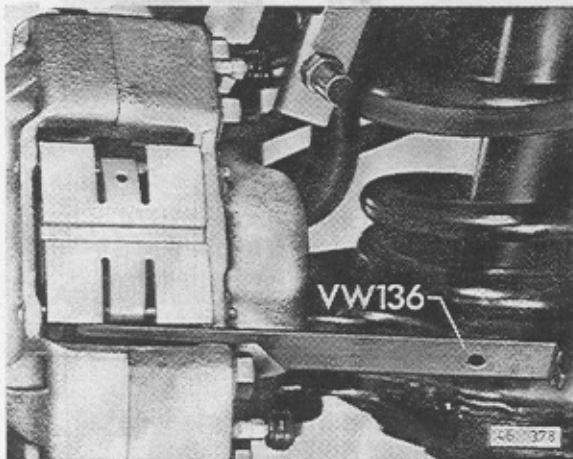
Bremsbelagdicke prüfen Bremssattel Fa. Girling
